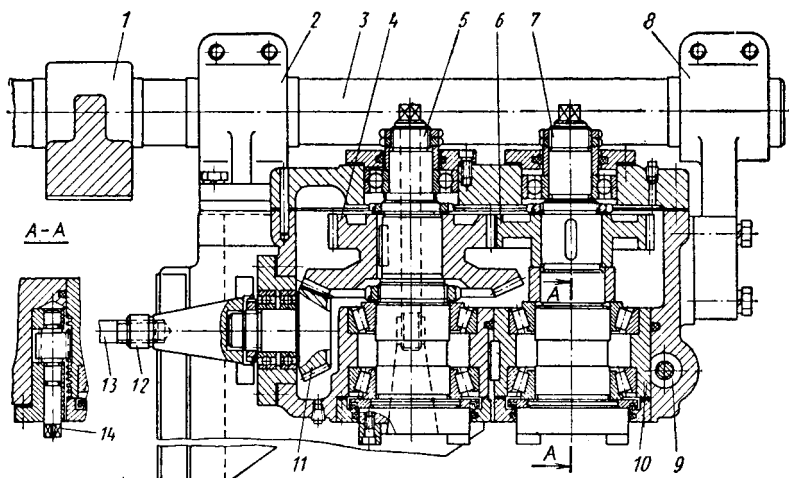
Двухшпindelная фрезерная головка к станку мод. 6Н82Г
